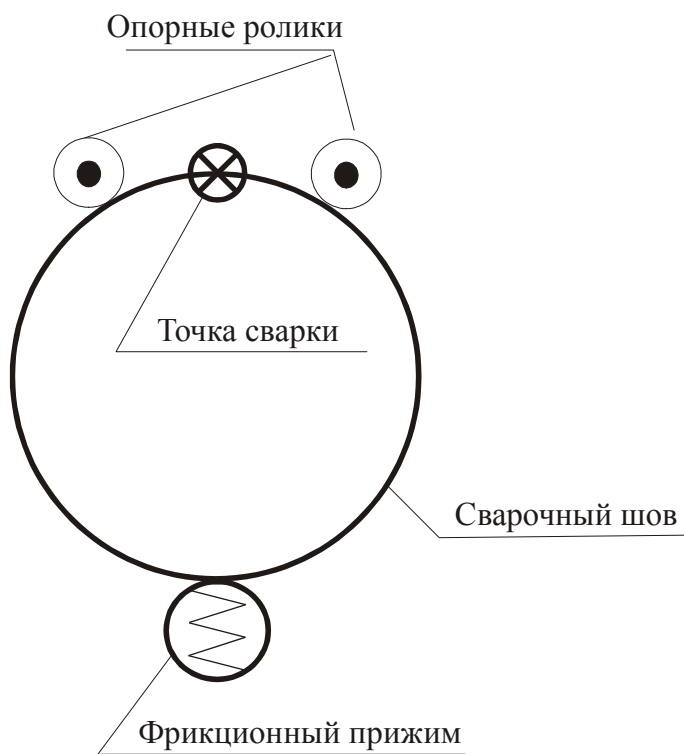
Схема фрикционного привода и позиционирования сварочного шва под луч лазера.
